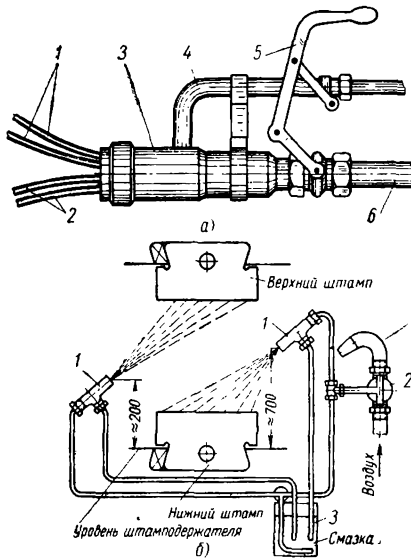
Приспособления для охлаждения штампов: а — соляным раствором: 1 — трубки для охлаждения верхнего штампа; 2 — то же для нижнего штампа; 3 — смешивательная камера; 4 — труба для воды; 5 — рукоятка; 6 — коллоидный графитом; 1 — распылитель; 2 — кран; 3 — бачок; 4 — сопло
